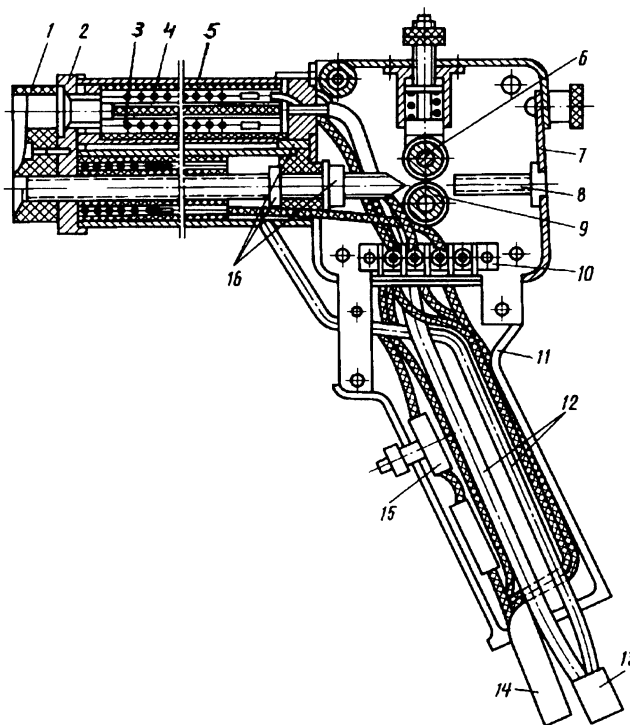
Ручной сварочный инструмент устройства РЭСУ-500Б:
